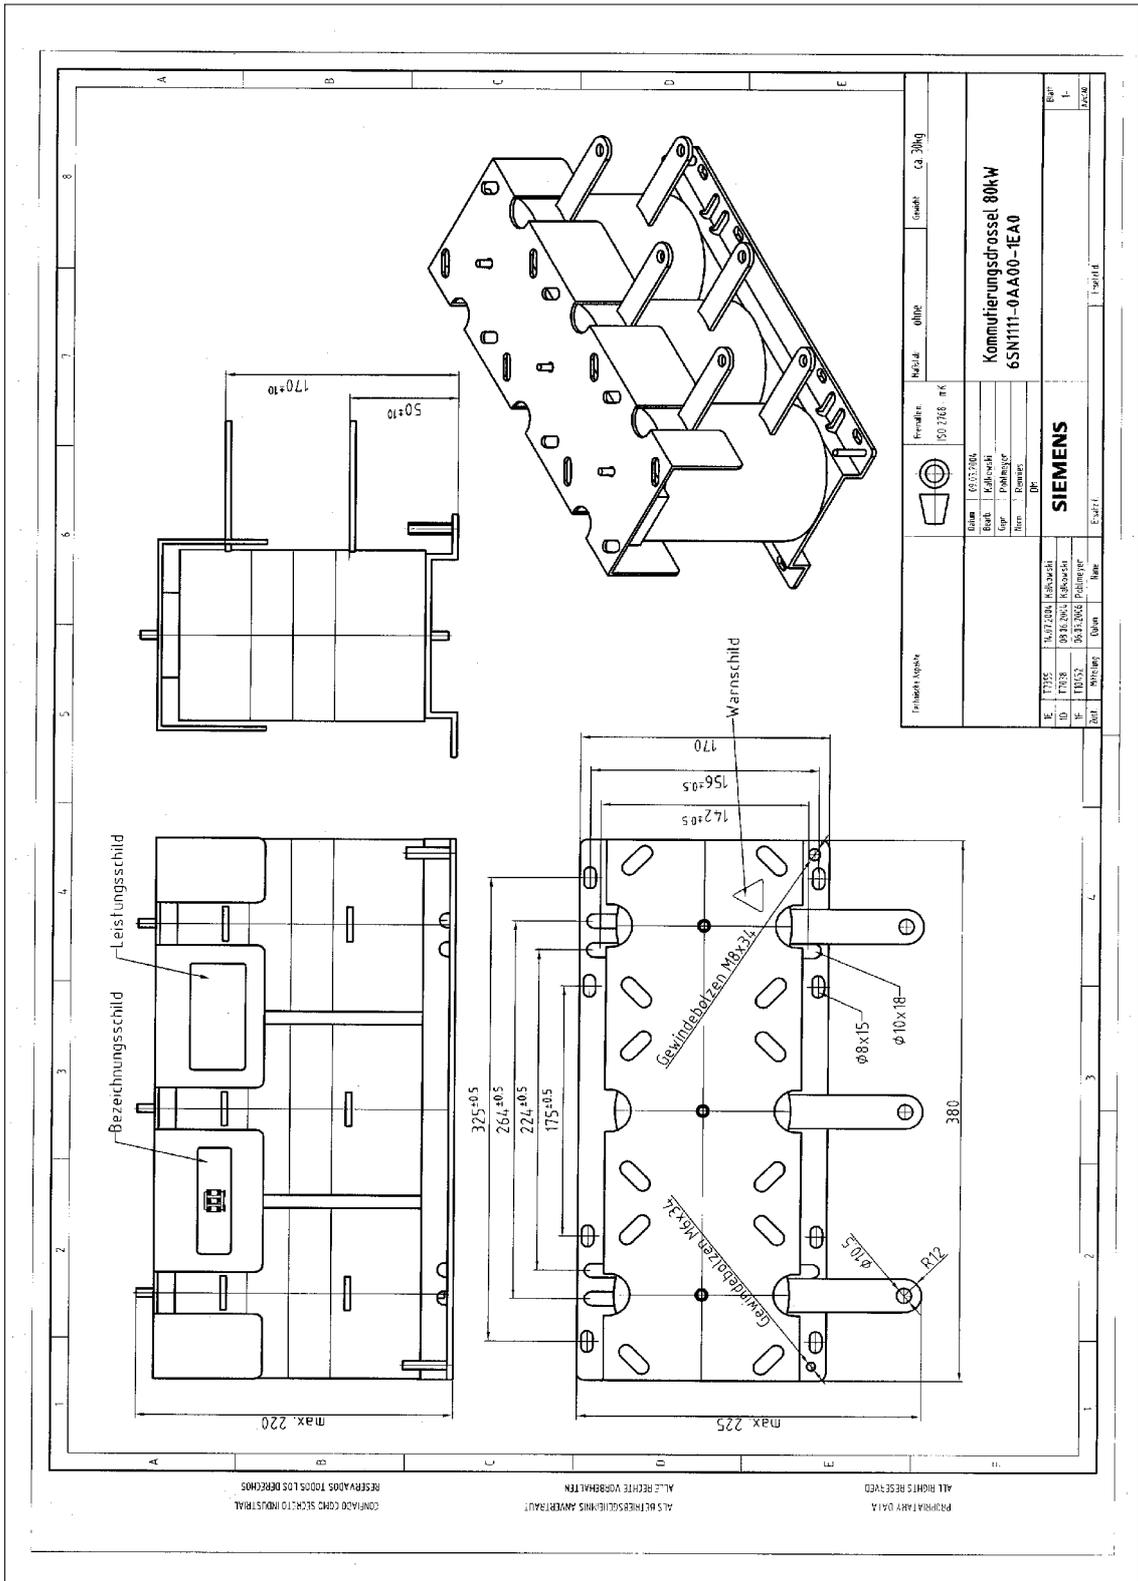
Bobina HF trifásica 80 kW, 6SN1111-0AA00-1EAx
